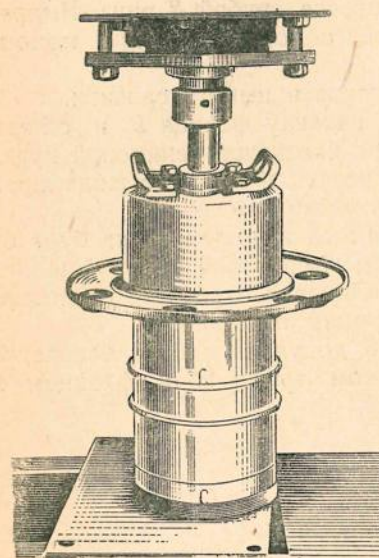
Запрессовка наружного кольца шарикоподшипника в ступицу нижнего катка
